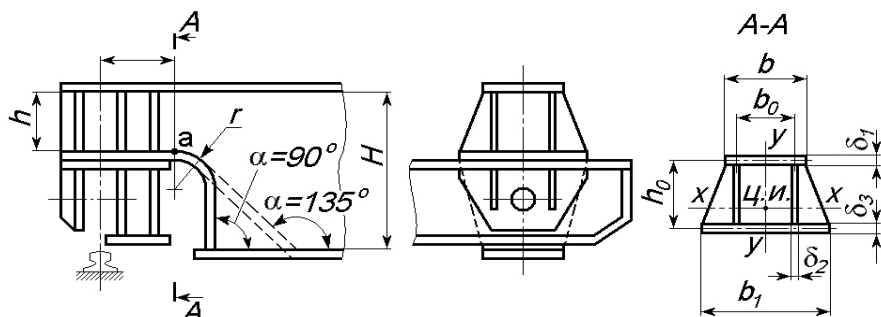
Схема к расчету опорного сечения пролетной балки
